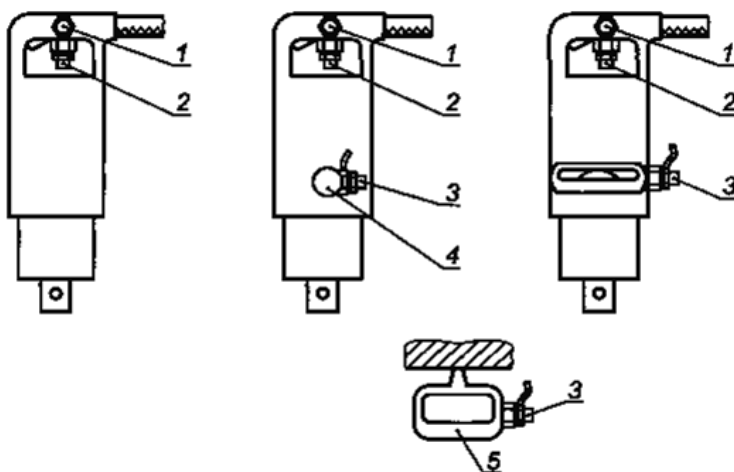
Ручная машина с рукояткой лучкового типа (поддерживающая рукоятка может присутствовать или отсутствовать; выходной вал может быть параллелен валу двигателя или находиться под углом к нему):
